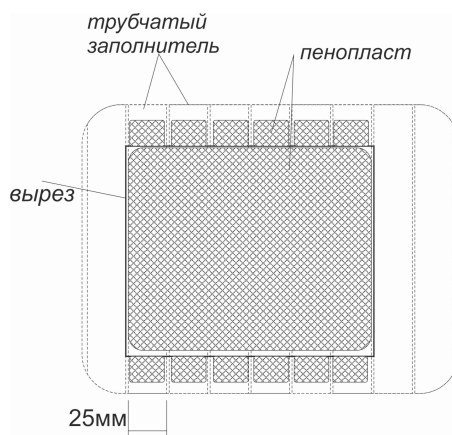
Конструктивно-технологическая схема установки пенопласта Rohacell A в трубчатый наполнитель
